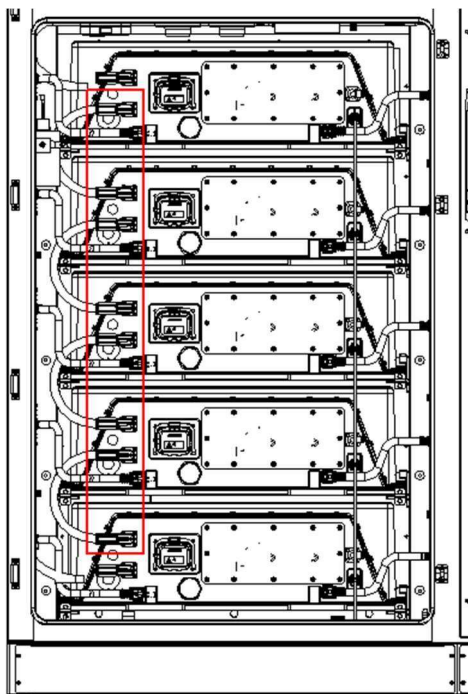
21 Instale los cables del paquete de baterías en secuencia
